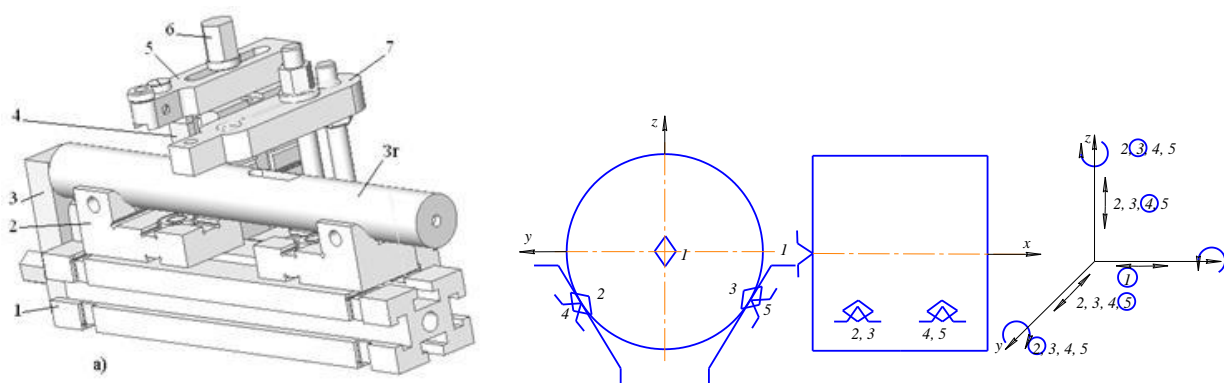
Технический рисунок макета зажимного станочного приспособления и схема базирования
